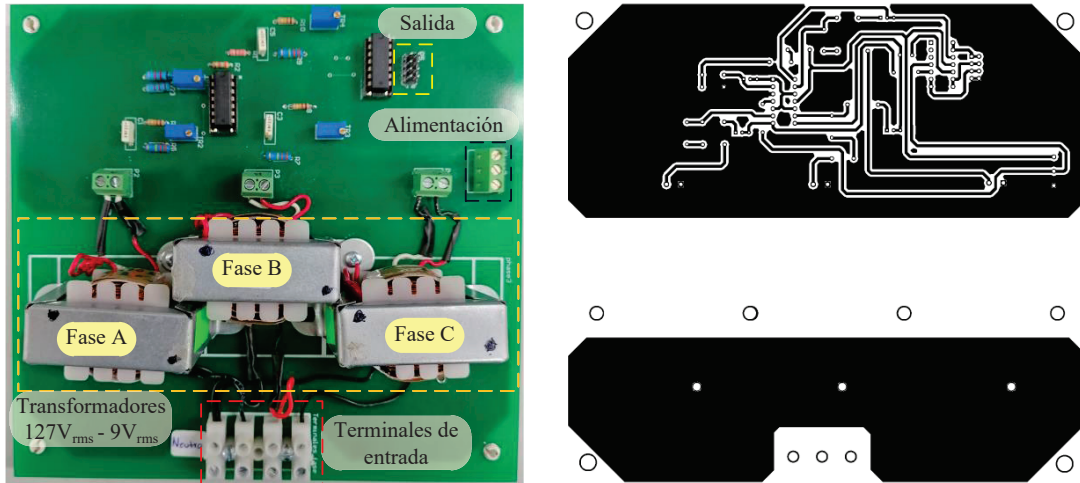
De izquierda a derecha, implementación física, diagrama de enrutado PCB de la tarjeta de sensado del voltaje.
